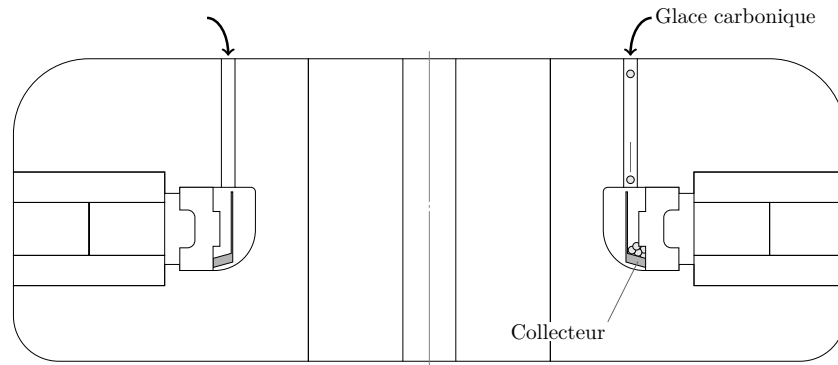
Pour démonter le circuit, on utilise un collecteur qui permet de stocker de la glace carbonique sous forme de paillettes au contact de la bague de positionnement.
